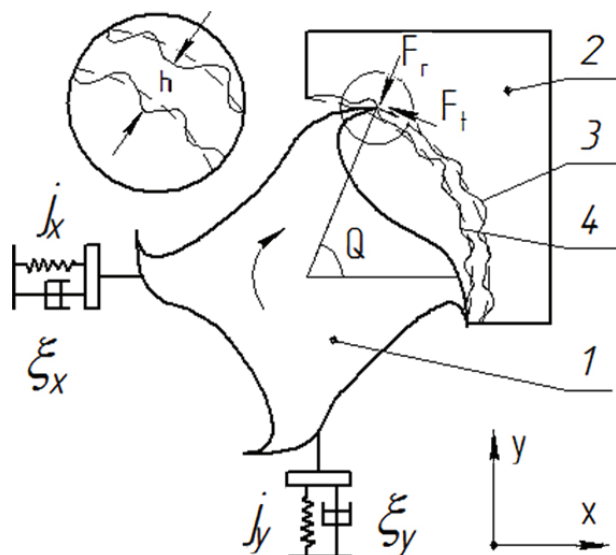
Механическая модель формирования профиля поверхности в процессе фрезерования при лимитировании фрезерной наладки (воспроизводится из работы [7, 8]): 1 — фреза; 2 — заготовка; 3 — поверхность после последующего реза; 4 — поверхность после предыдущего реза
